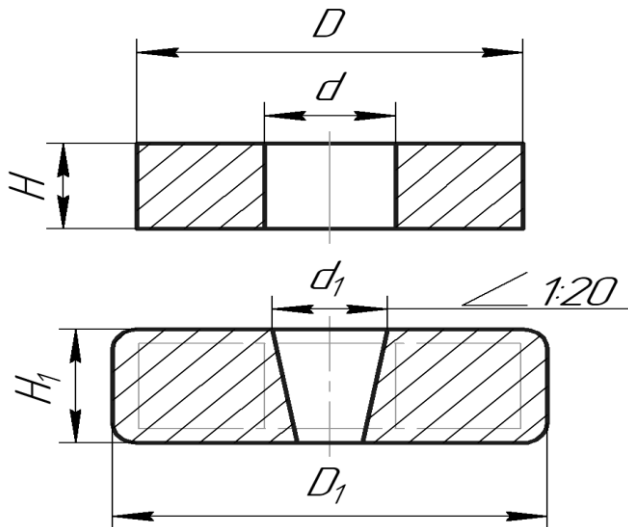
Чертеж изделия с отверстием и поковки этого изделия
